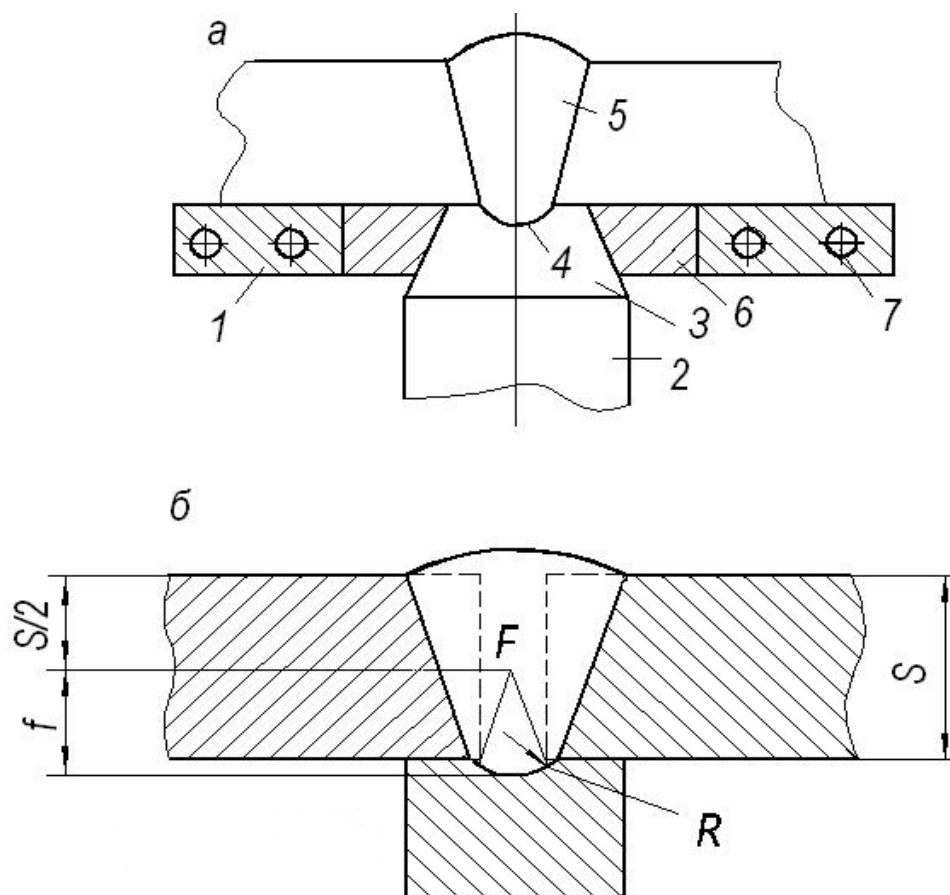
Устройство для формирования: а - обратная сторона сварного шва; б - формирующая канавка: R - радиус формирующей канавки; S - толщина свариваемых деталей; F - фокусное расстояние
